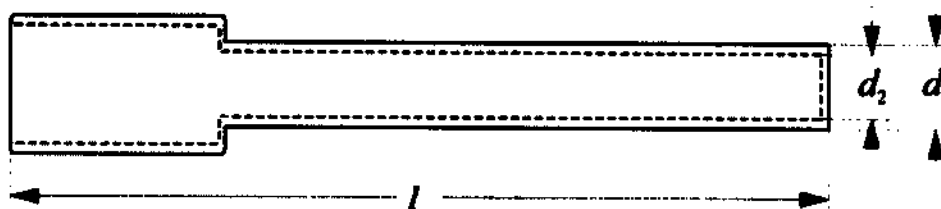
Схема общего вида защитного колпачка для иглы
